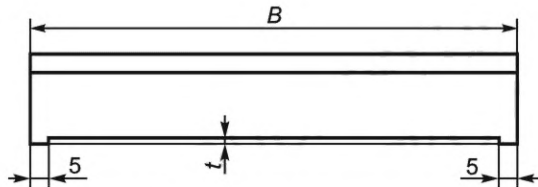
Шаблон контроля профиля поверхности катания головки рельса
